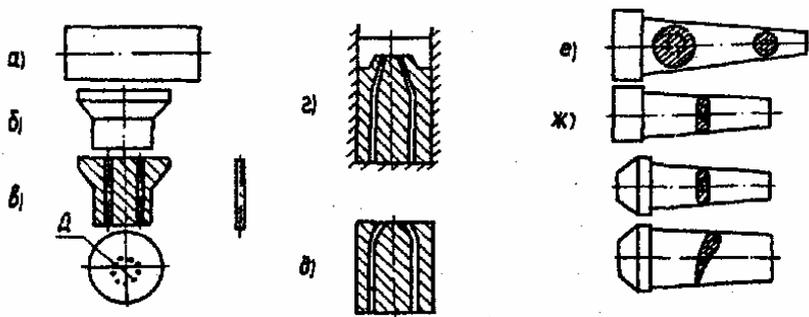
Изготовление многоканальной (сотовой) охлаждаемой лопатки турбины: *а* – исходная заготовка; *б* – высадка головки; *в* – обработка отверстий и закладка в них заполнителя; *г* – прессование грибовидной заготовки на цилиндре; *д* – отрезка верхней части; *е* – выдавливание конусной заготовки; *ж* – объемная штамповка
